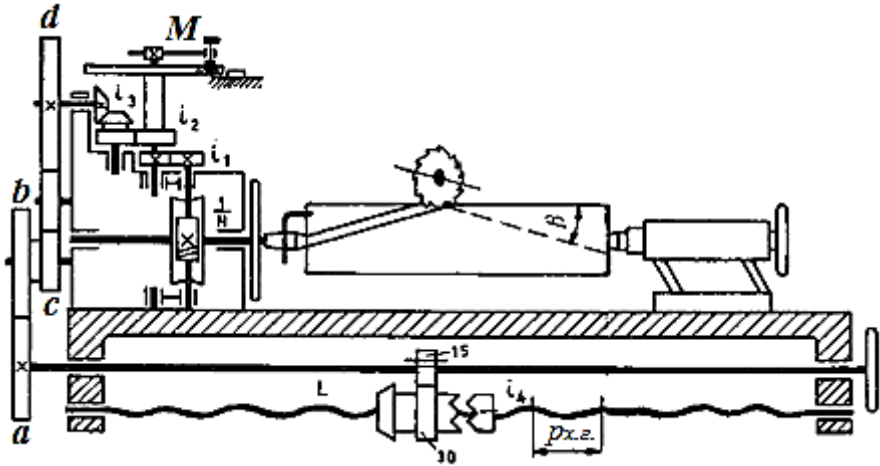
Налаштування верстата на фрезерування гвинтових канавок
